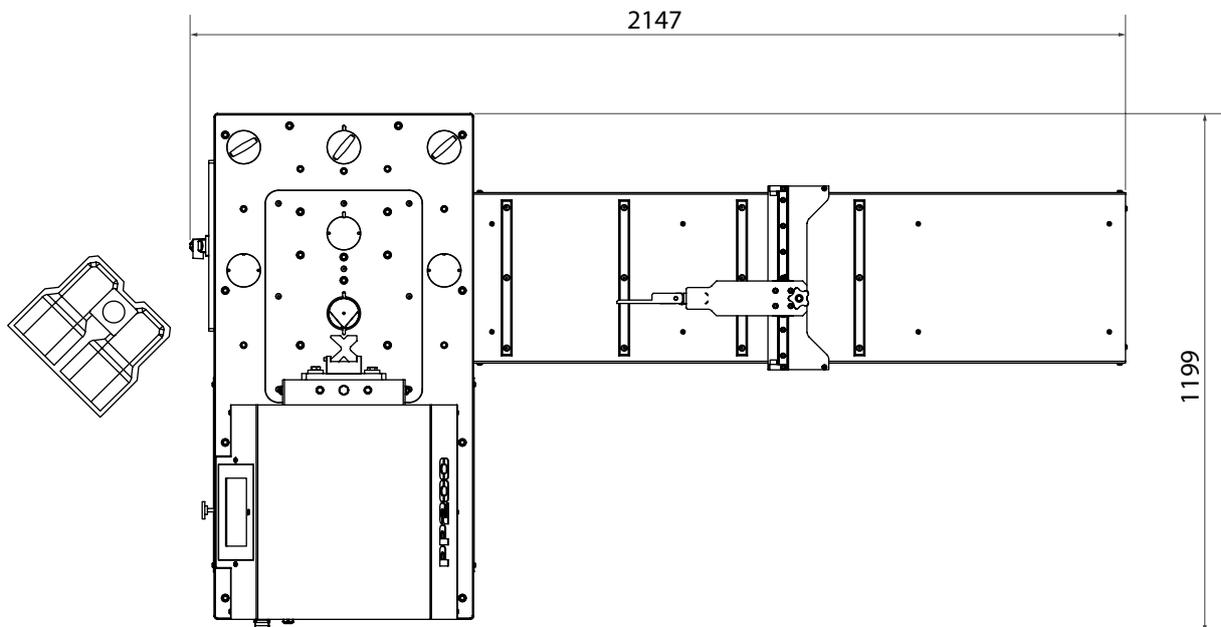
Layout y Dimensiones de la PP200CNC + Tope
